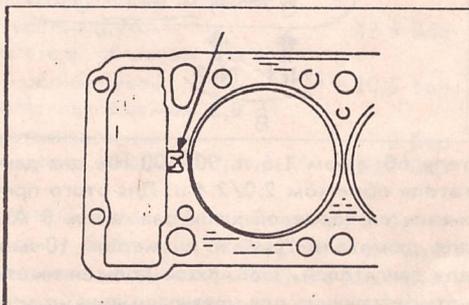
Маркировка уплотнительной прокладки (показана стрелкой).
